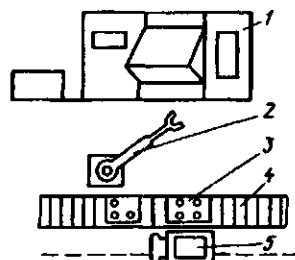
Гибкий производственный модуль с промышленным роботом: 1 – станок с ЧПУ; 2 – промышленный робот; 3 – кассета с заготовками; 4 – конвейер-накопитель; 5 – робокара
